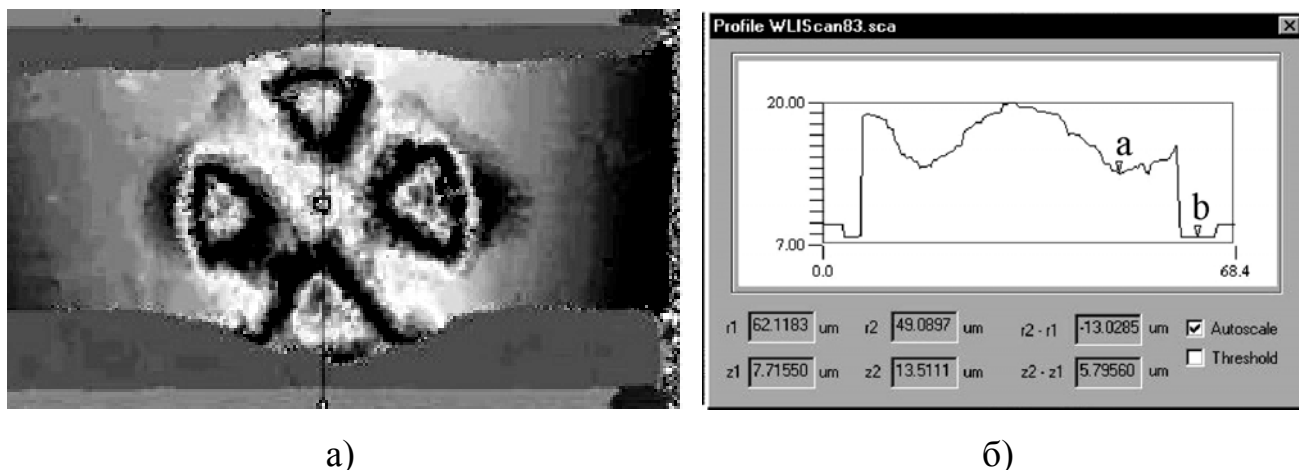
Зварне з'єднання (а) та профіль зварного з'єднання (б)
